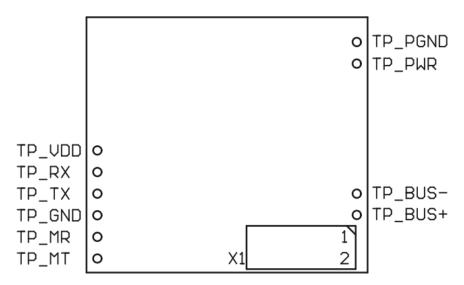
Draufsicht auf MBUS-M13 mit Anschlüssen
